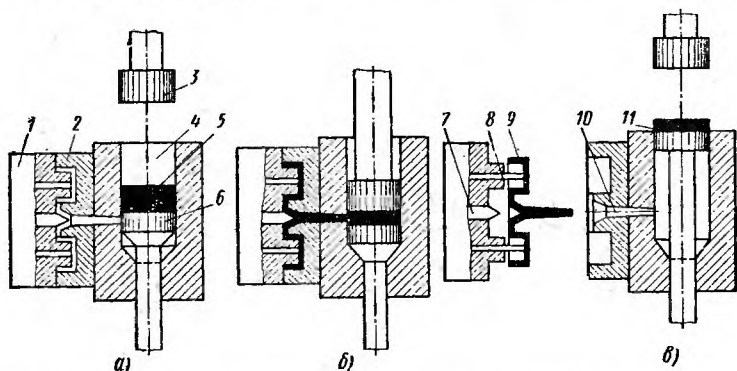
Схема процесса литья под давлением на машинах с вертикальной камерой прессования:
